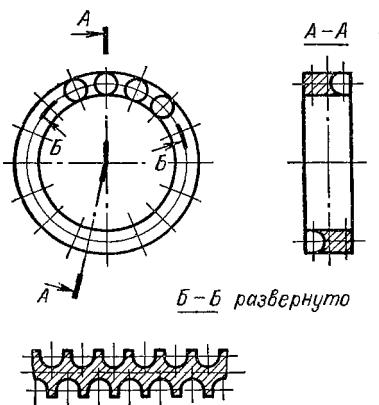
Сечение цилиндрической поверхностью, развертываемой в плоскость
